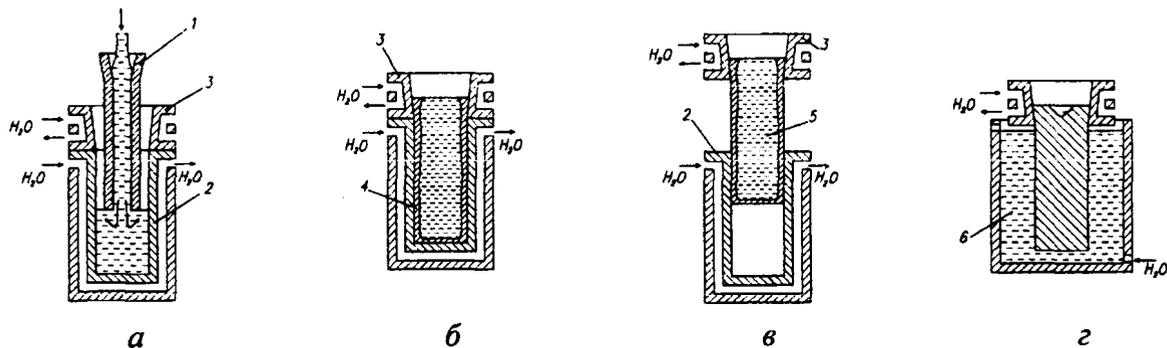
Схема получения отливок методом литья закалочным затвердеванием 1 – заливочное устройство; 2 – стационарный кристаллизатор; 3 – подвижный кристаллизатор; 4 – стакан; 5 – расплав; б – закалочная ванна;
